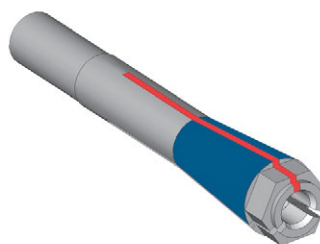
ENGRASAR LA PINZA DE SUJECIÓN; LA SUPERFICIE A LA QUE SE DEBE APLICAR GRASA APARECE MARCADA EN AZUL; LA RANURA QUE NO DEBE ENGRASARSE APARECE MARCADA EN ROJO
